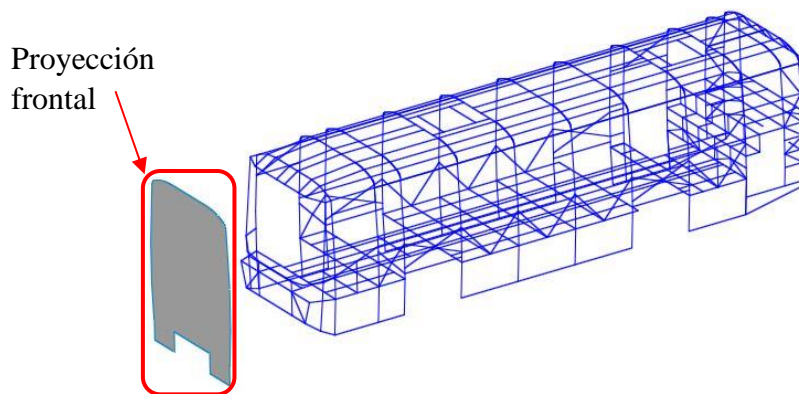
Proyección frontal de la sección perpendicular al movimiento.
